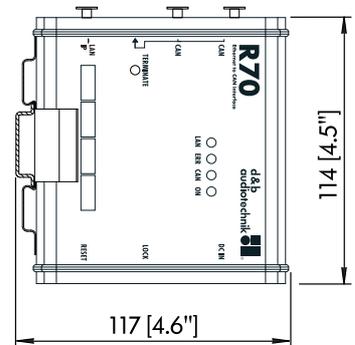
Montaje en raíl en forma de sombrero con dimensiones en mm [pulgadas]
